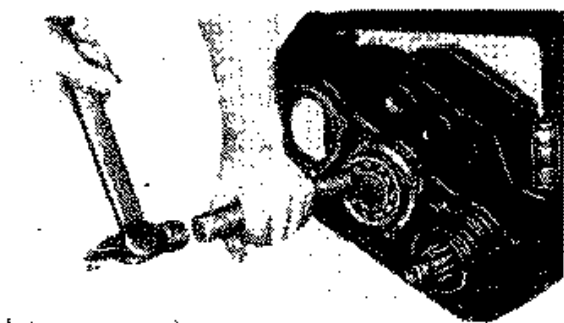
Запрессовка переднего подшипника промежуточного вала в отверстие картера на шейку вала
